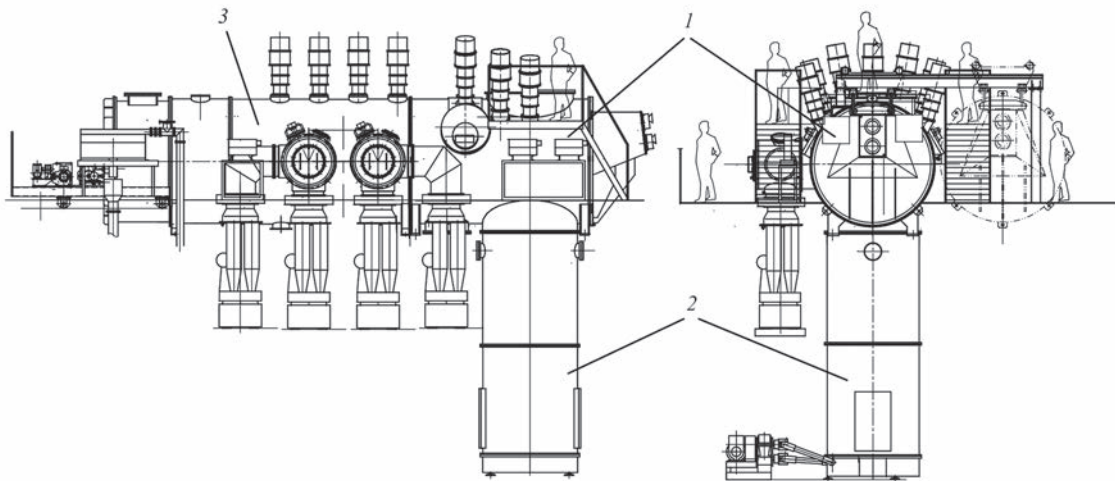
Конструкція електронно-променевої установки UE-5810: 1 — камера плавки; 2 — камера витягування; 3 — камера заготовки/опалення
